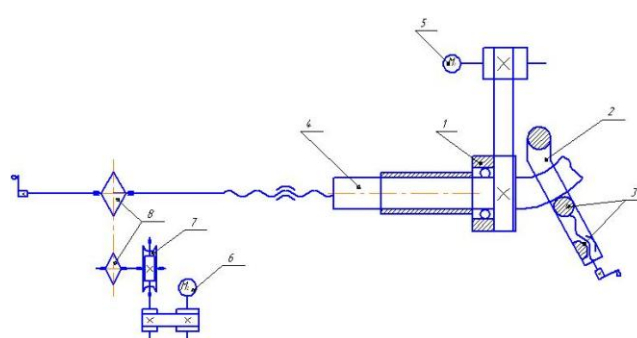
Кинематическая схема станка для гибки труб с обкатыванием
